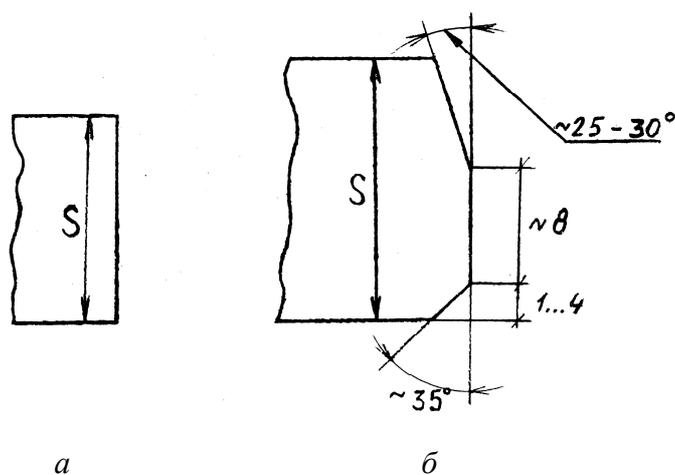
Виды разделки кромок при сварке под слоем флюса:
